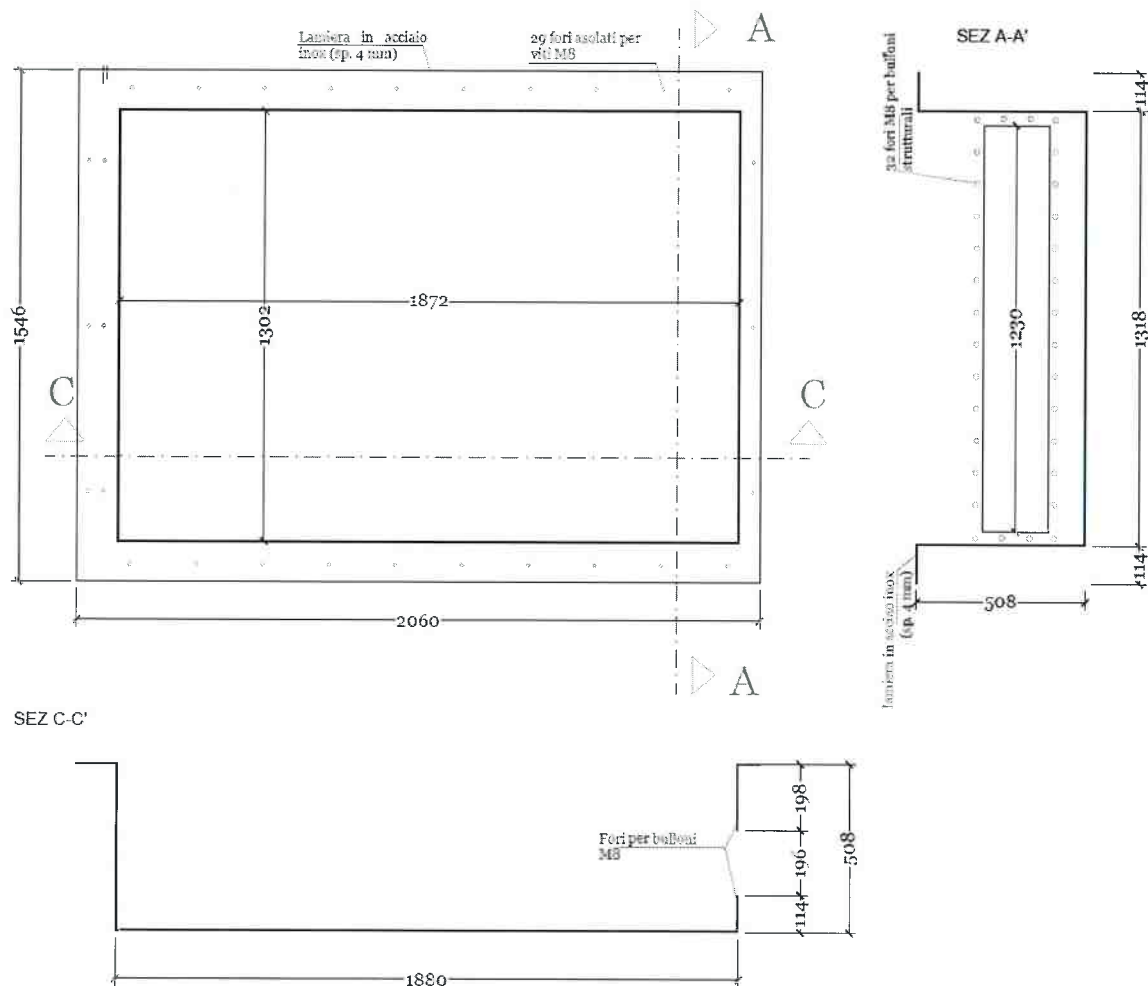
Vista in pianta e sezioni dell'elemento costruttivo: vasca tipo 2
